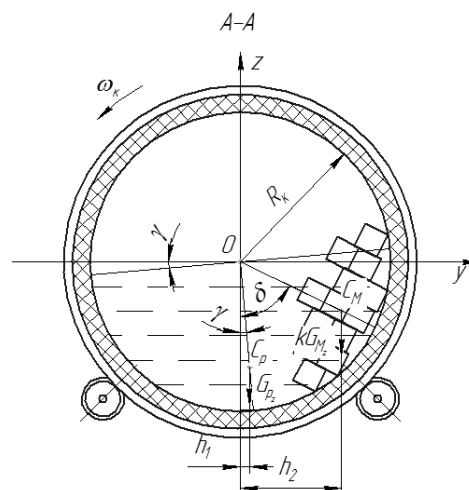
Схема расположения центра масс шихты в корпусе модели конвертера
